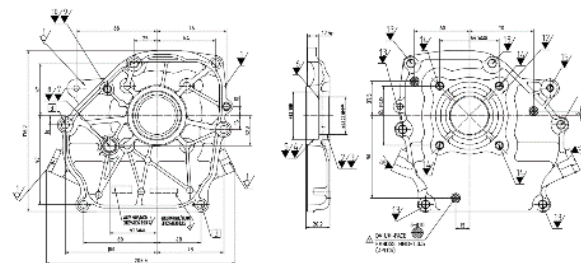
Layout baru *fixture* untuk produk *cover crankcase* dan *cylinder head
